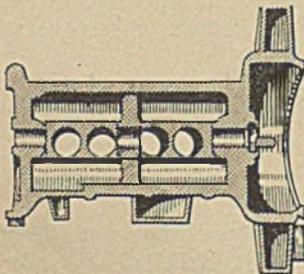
Zylinderblock ohne Kopf, Innenansicht, bei den billigeren amerikanischen Motoren gebräuchlich.
